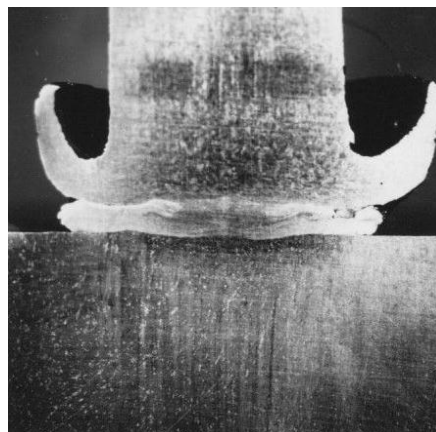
Схема формирования соединения при Т-образной сварке:
